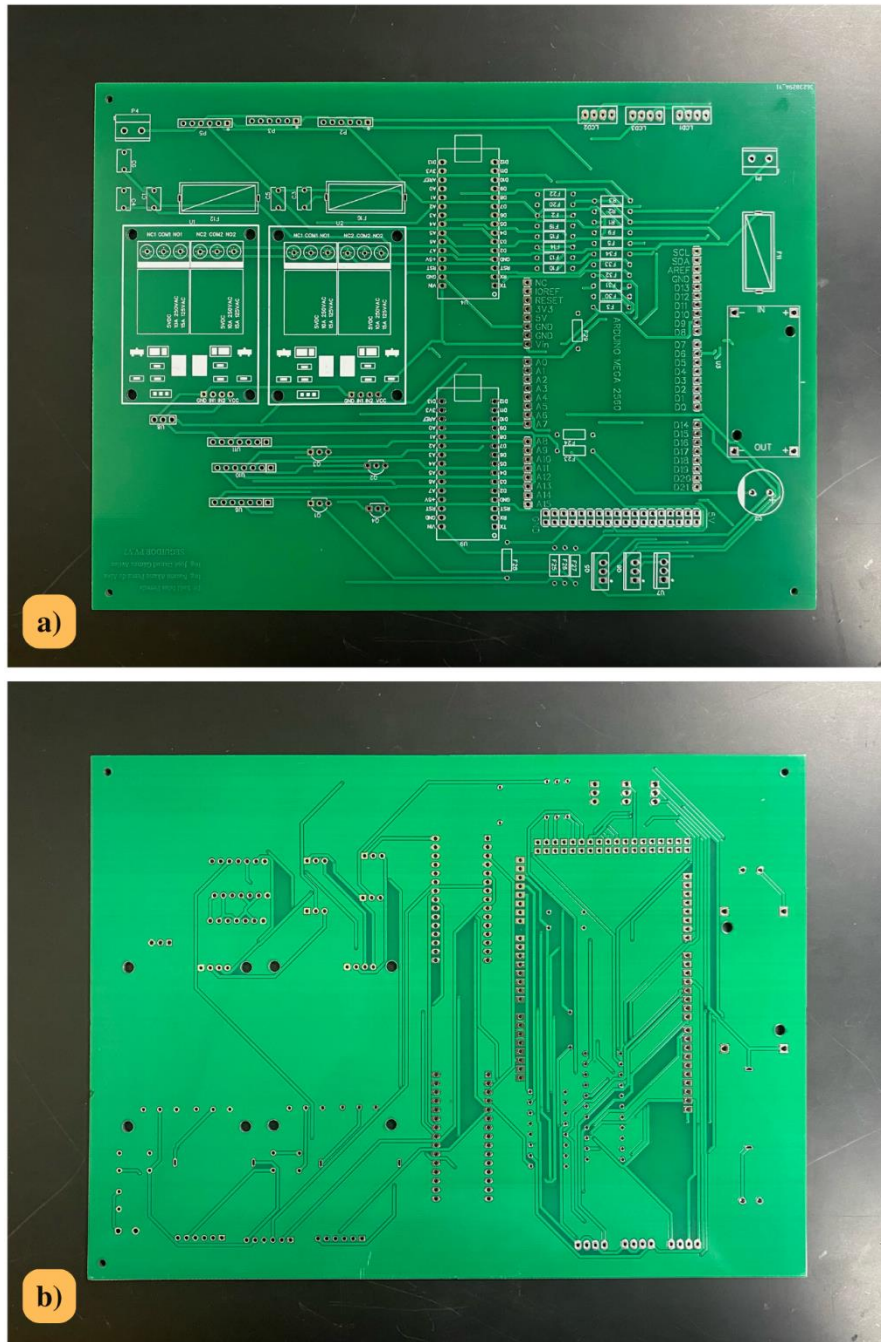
a) Vista frontal de la placa de circuito impreso del prototipo. b) Vista posterior de la placa de circuito impreso del prototipo.
